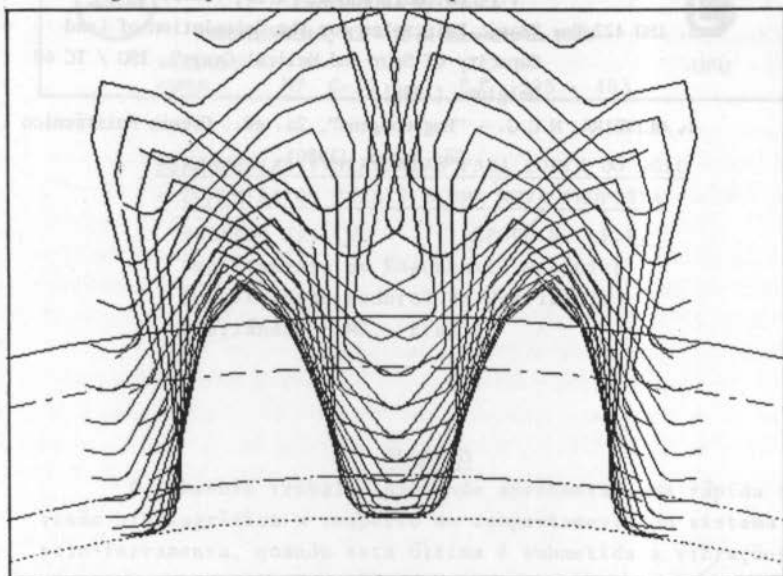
Evolução da fresa caracol durante a geração da engrenagem par de 39 dentes e forma final do dente
